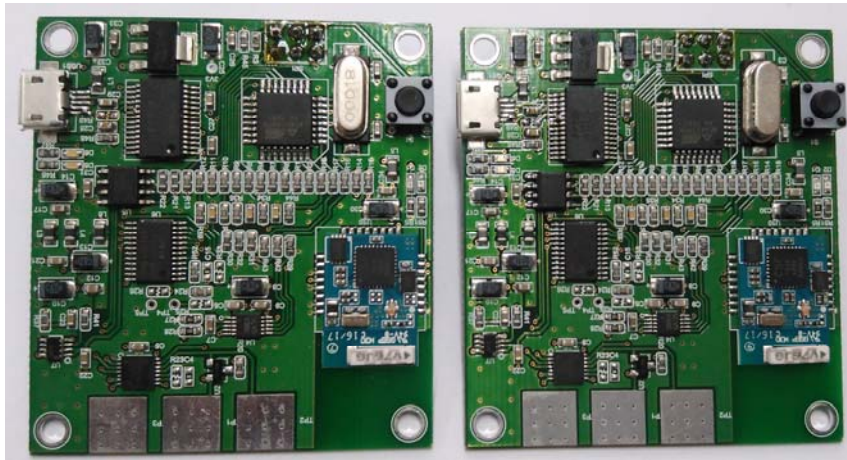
전용 IC를 사용하여 제작된 보드의 Top Layer PCB
